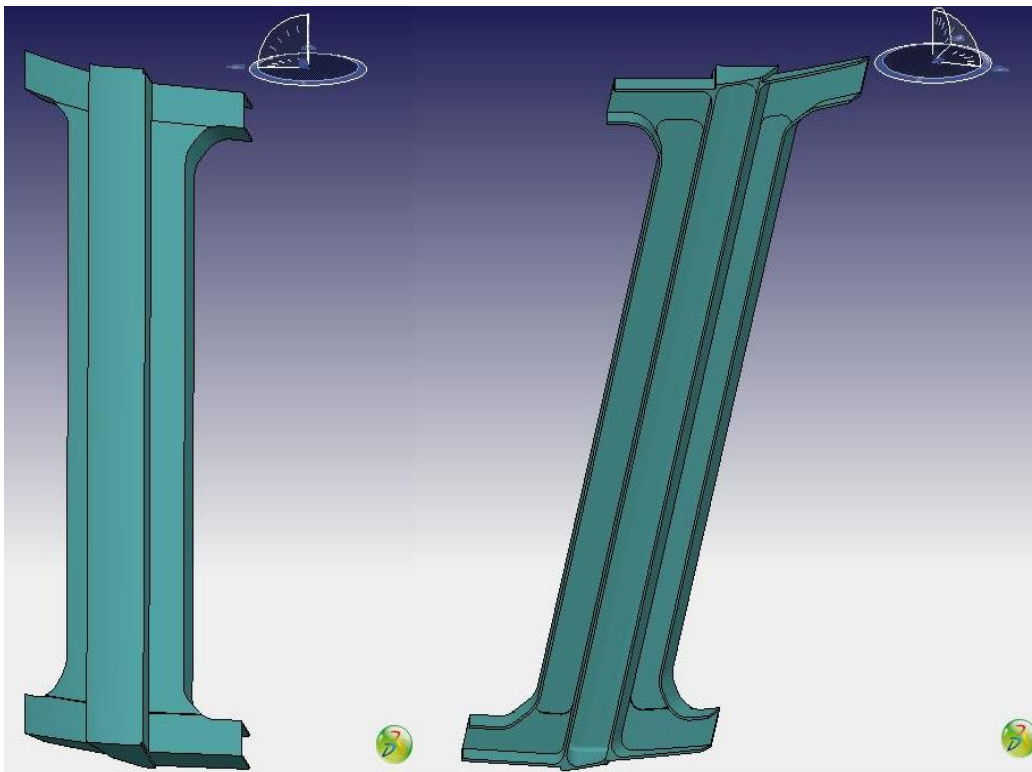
Proposta de alteração da viga lateral da estrutura.
